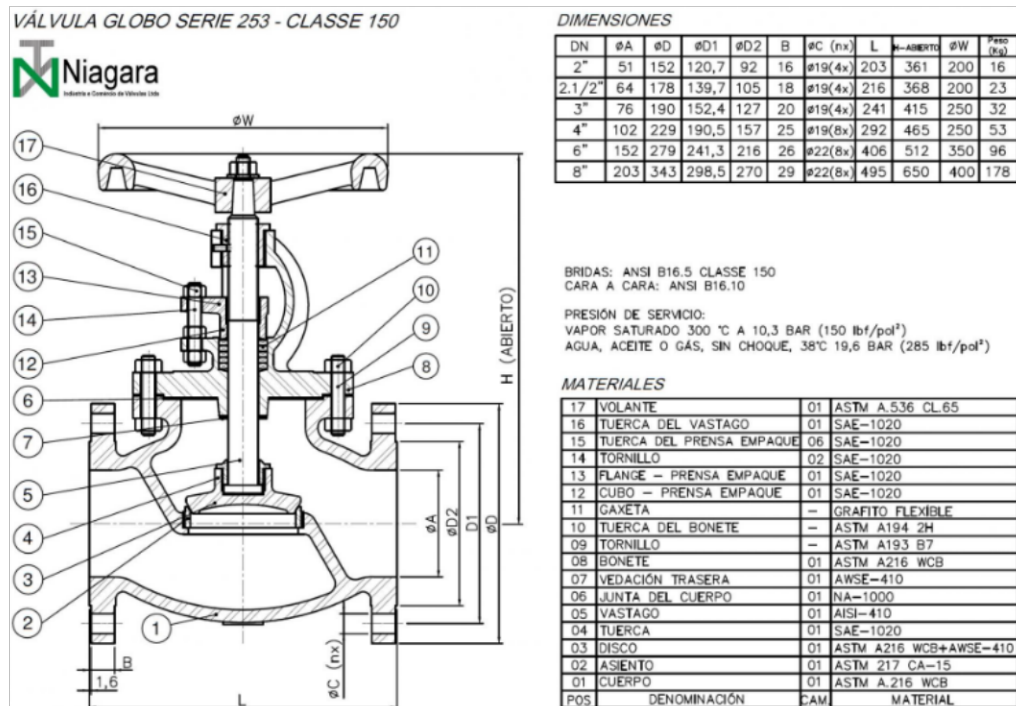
Dimensiones de la válvula globo serie 253. [16]
